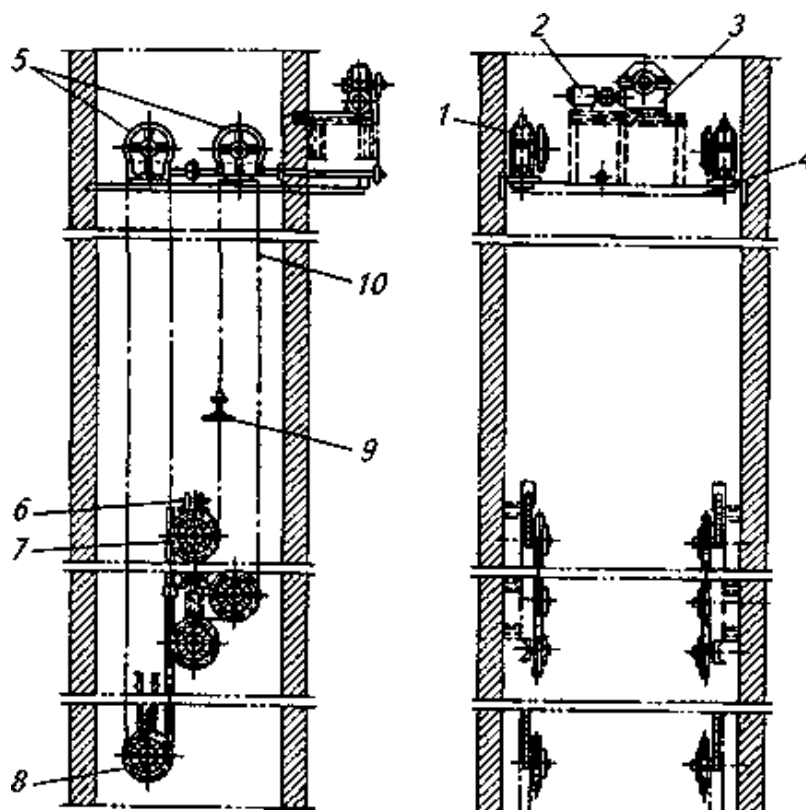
Малая автокоптелка АМ-3601, 3 – редукторы; 2 – электродвигатель; 4 – цепная передача; 5, 7, 8 – звездочки; 6 – натяжная станция; 9 – траверсы; 10 – цепи.
